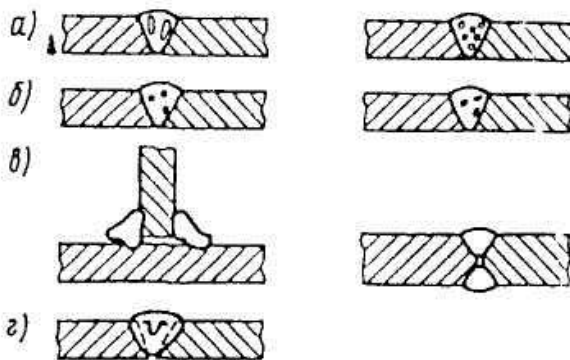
Наружные и внутренние дефекты сварного шва:
